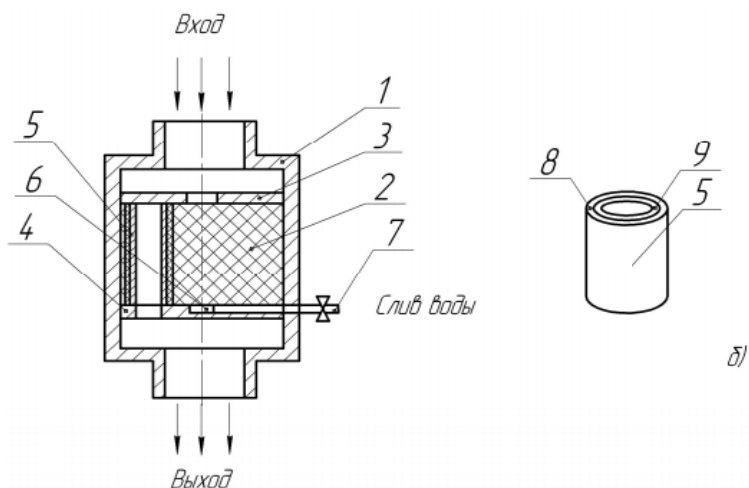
Фильтр сепаратор: 1 – корпус; 2 – пакет фильтрующего материала; 3, 4 – распределительные решетки; 5 – двухслойные трубчатые фильтроэлементы; 6 – коаксиальные каналы; 7 – сливное отверстие; 8 – слой из спеченного порошкового материала; 9 – слой из гидрофобного материала
